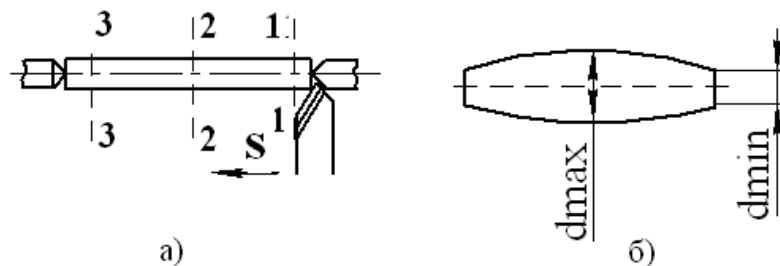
Закріплення заготовки в центрах (заготовка менш жорстка, ніж верстат)
